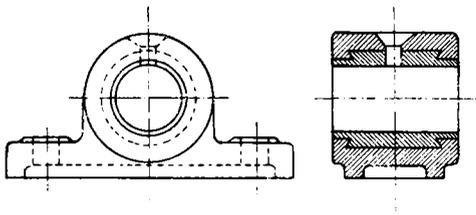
Augenlager mit eingegossener Weißmetall-Schale.
